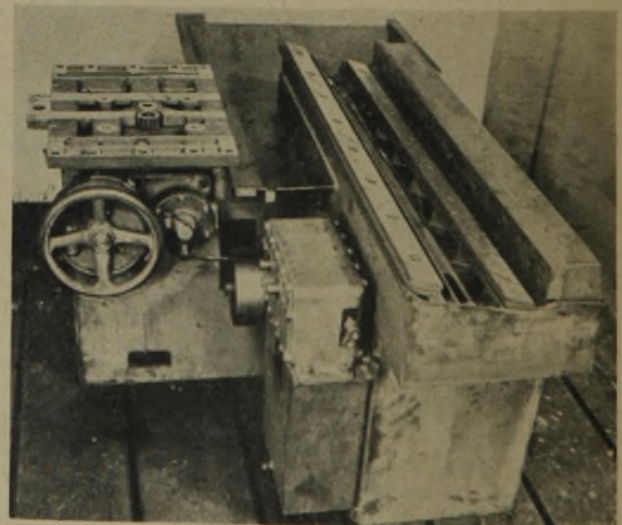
Bett einer mittleren Schleifmaschine mit aufgebrachten Führungsbahnen
